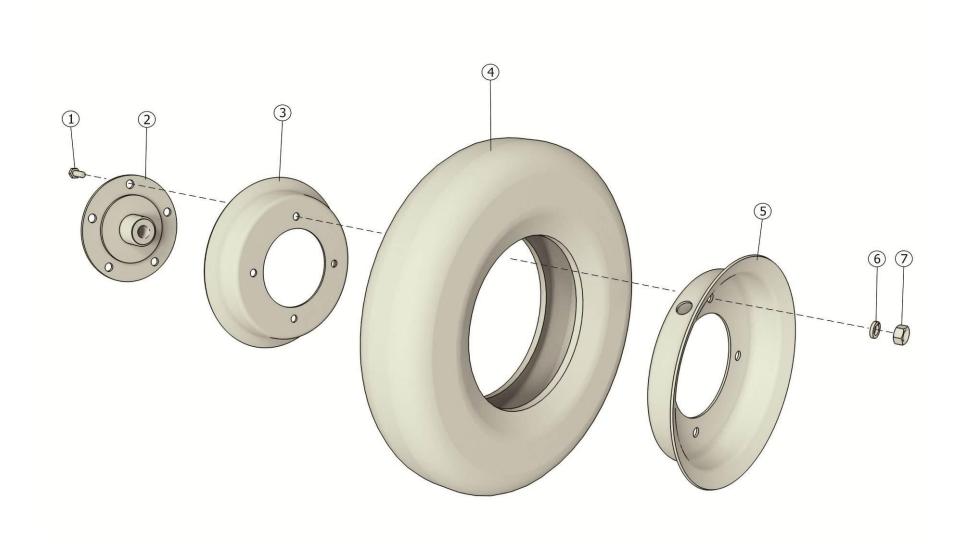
Колесо в сборе МЗС-90.01.100
